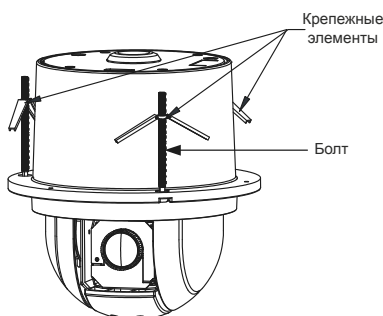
Установка крепежных элементов для врезного монтажа
